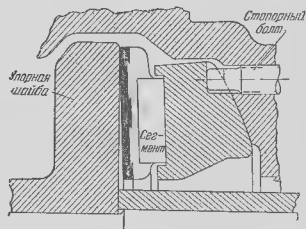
Неправильная установка стопорного болта сегментного подшипника ЛМЗ прежних выпусков.
